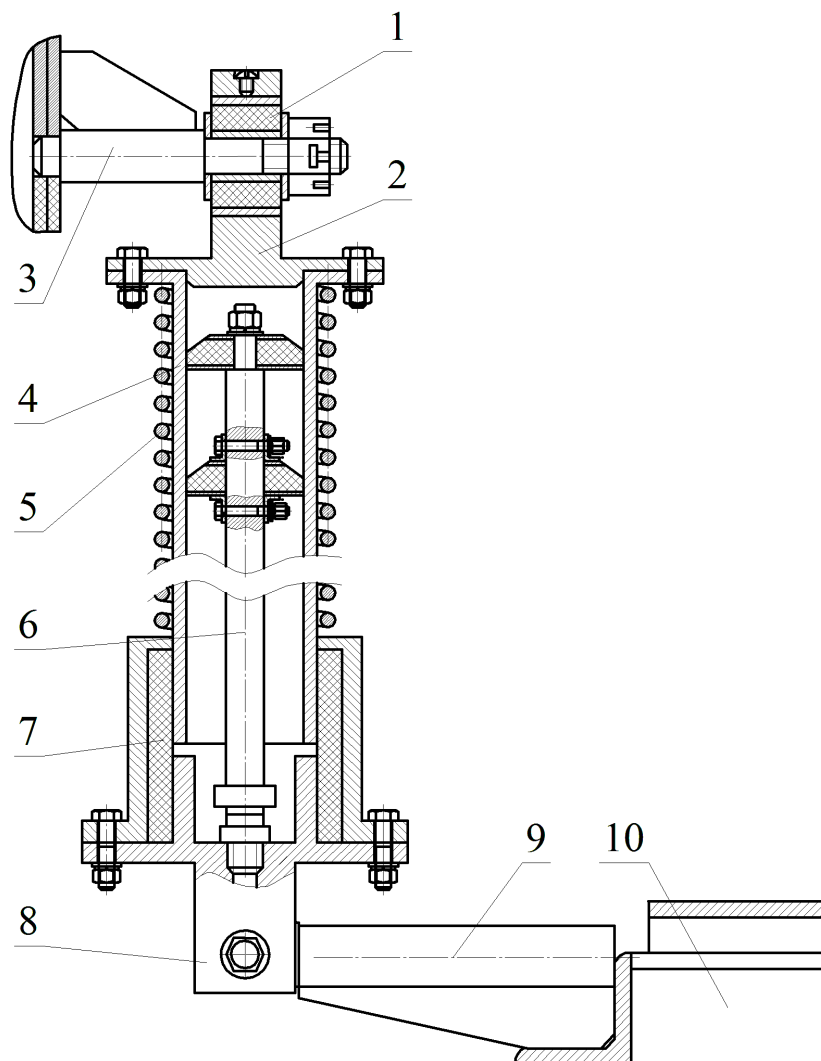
Розпірна штанга: 1 – резинова втулка; 2 – верхня провушина; 3 – палець; 4 – телескопічна труба; 5 – пружина стиснення; 6 – напрямляючий шток; 7 – капроновий стакан; 8 – нижня провушина; 9 – палець; 10 – нерухома рама двигуна
